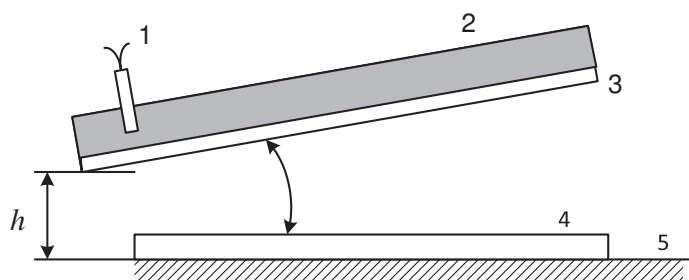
Схема сварки взрывом под углом α : 1 — детонатор, 2 — заряд ВВ, 3 — метаемая пластина, 4 — неподвижная пластина, 5 — опора.
